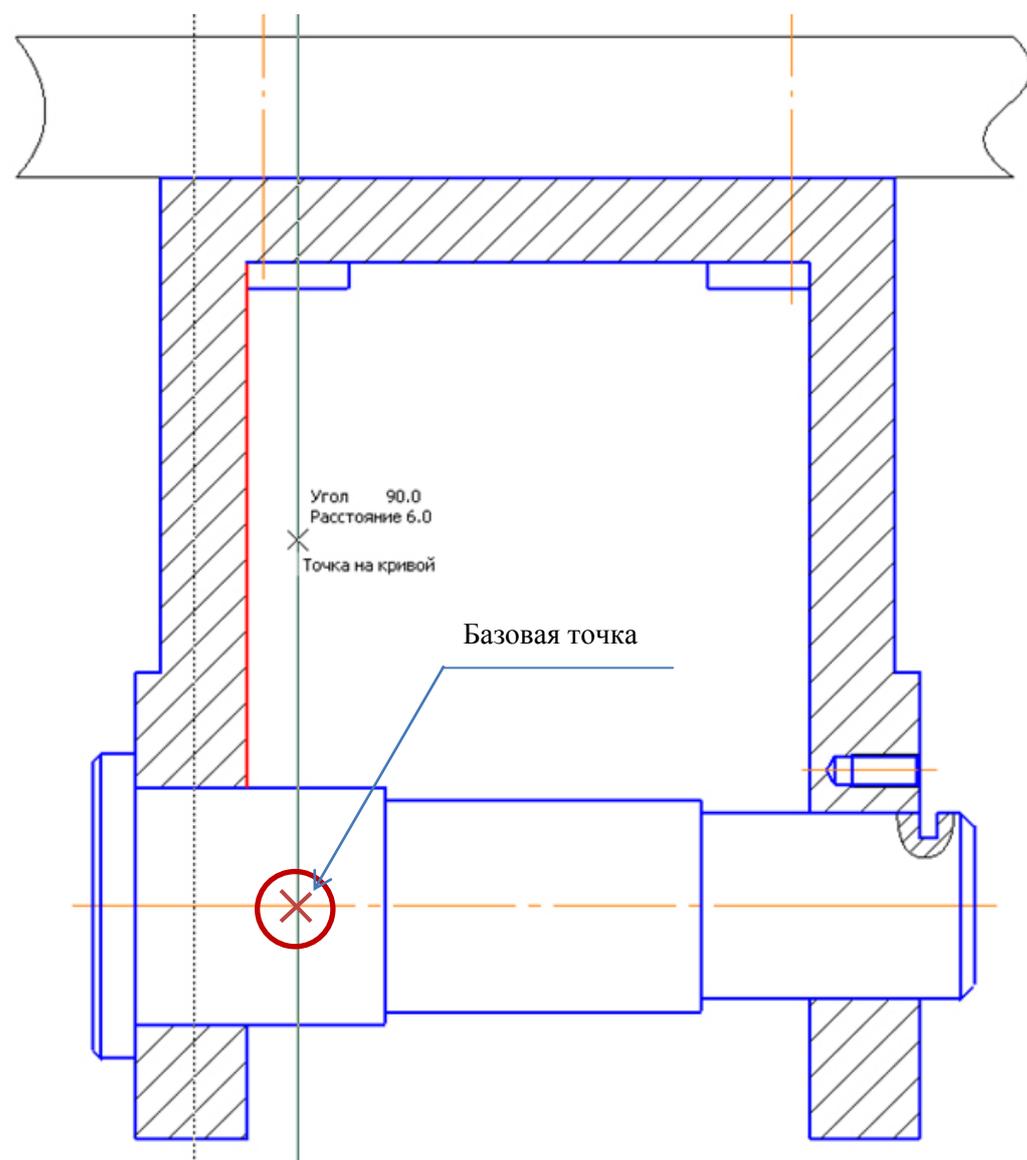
Базовая точка для установки сборочной единицы «Колесо»
